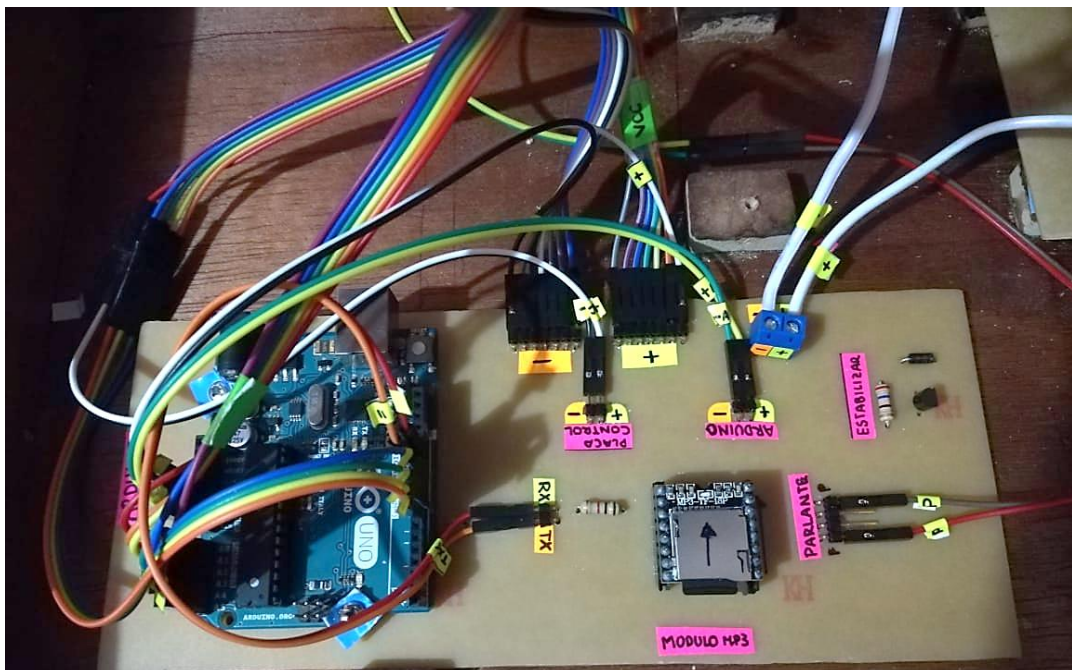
Acabado y soldadura de los elementos en la placa memoria principal
